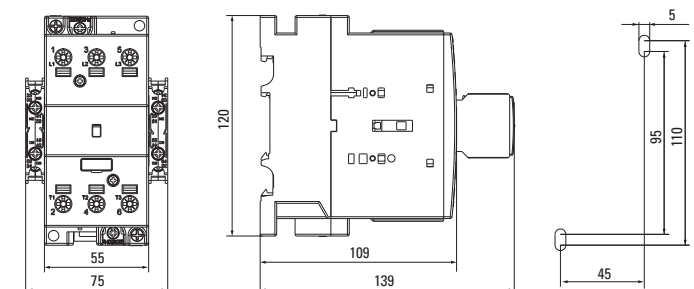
Габаритные и установочные размеры контакторов KM3 50A, KM3 60A, KM3 65A
